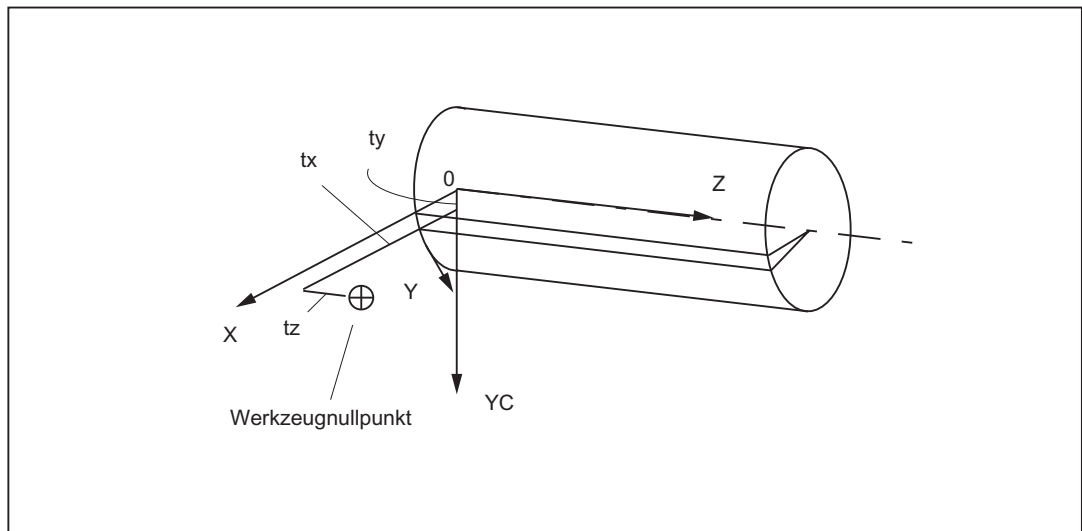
Lage des Werkzeugnullpunktes zum Nullpunkt der Maschine
